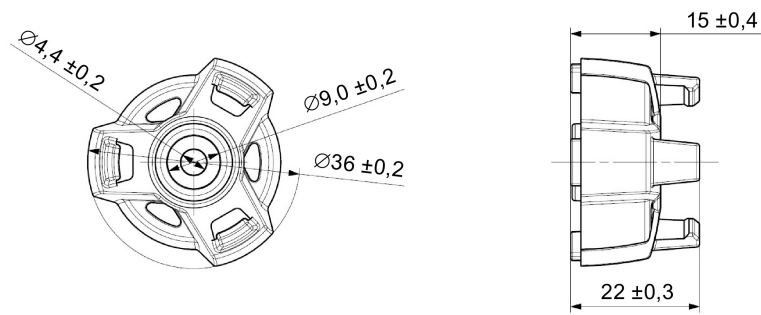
Desenho de dimensões do espaçador 6GT2690-0AK00
